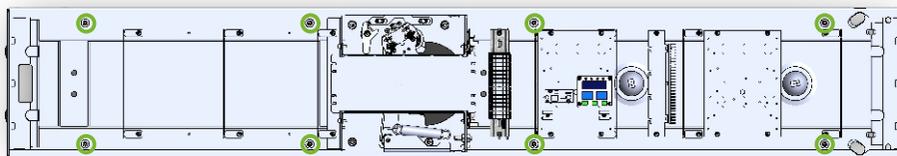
Места соединения винтами основания крышки корпуса механизма (вид сверху)
